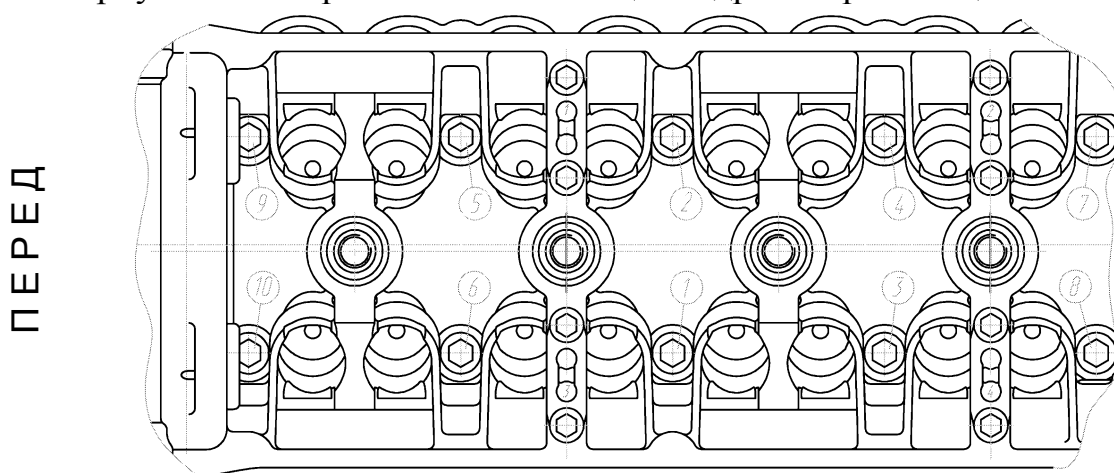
Последовательность затяжки болтов крепления головки цилиндров
